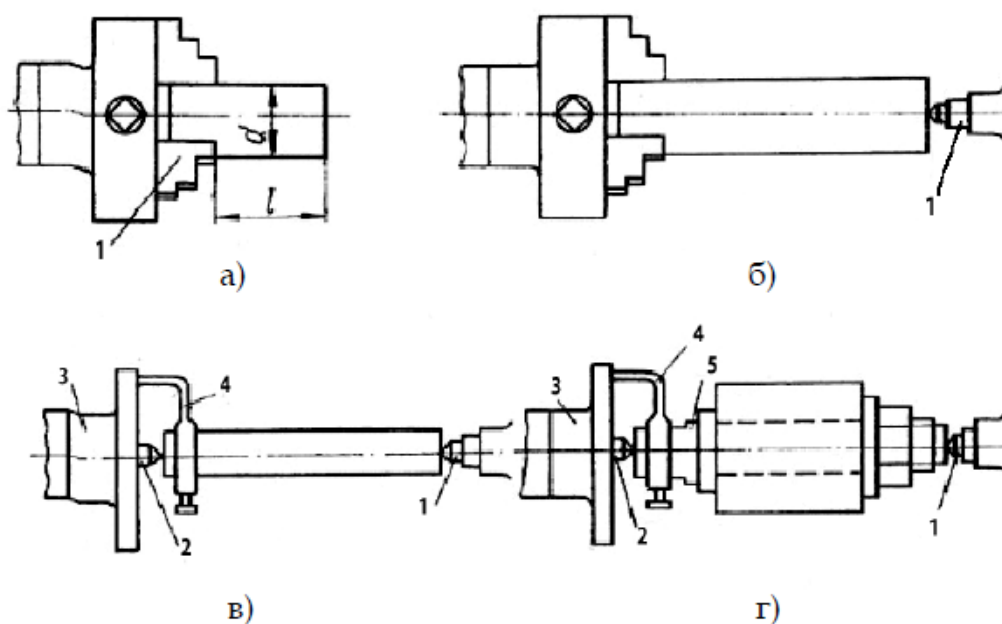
Установка деталі на ТВ: а – установка заготовки в патроні; б – закріплення заготовки у самоцентруючому патроні; в – закріплення заготовки в
